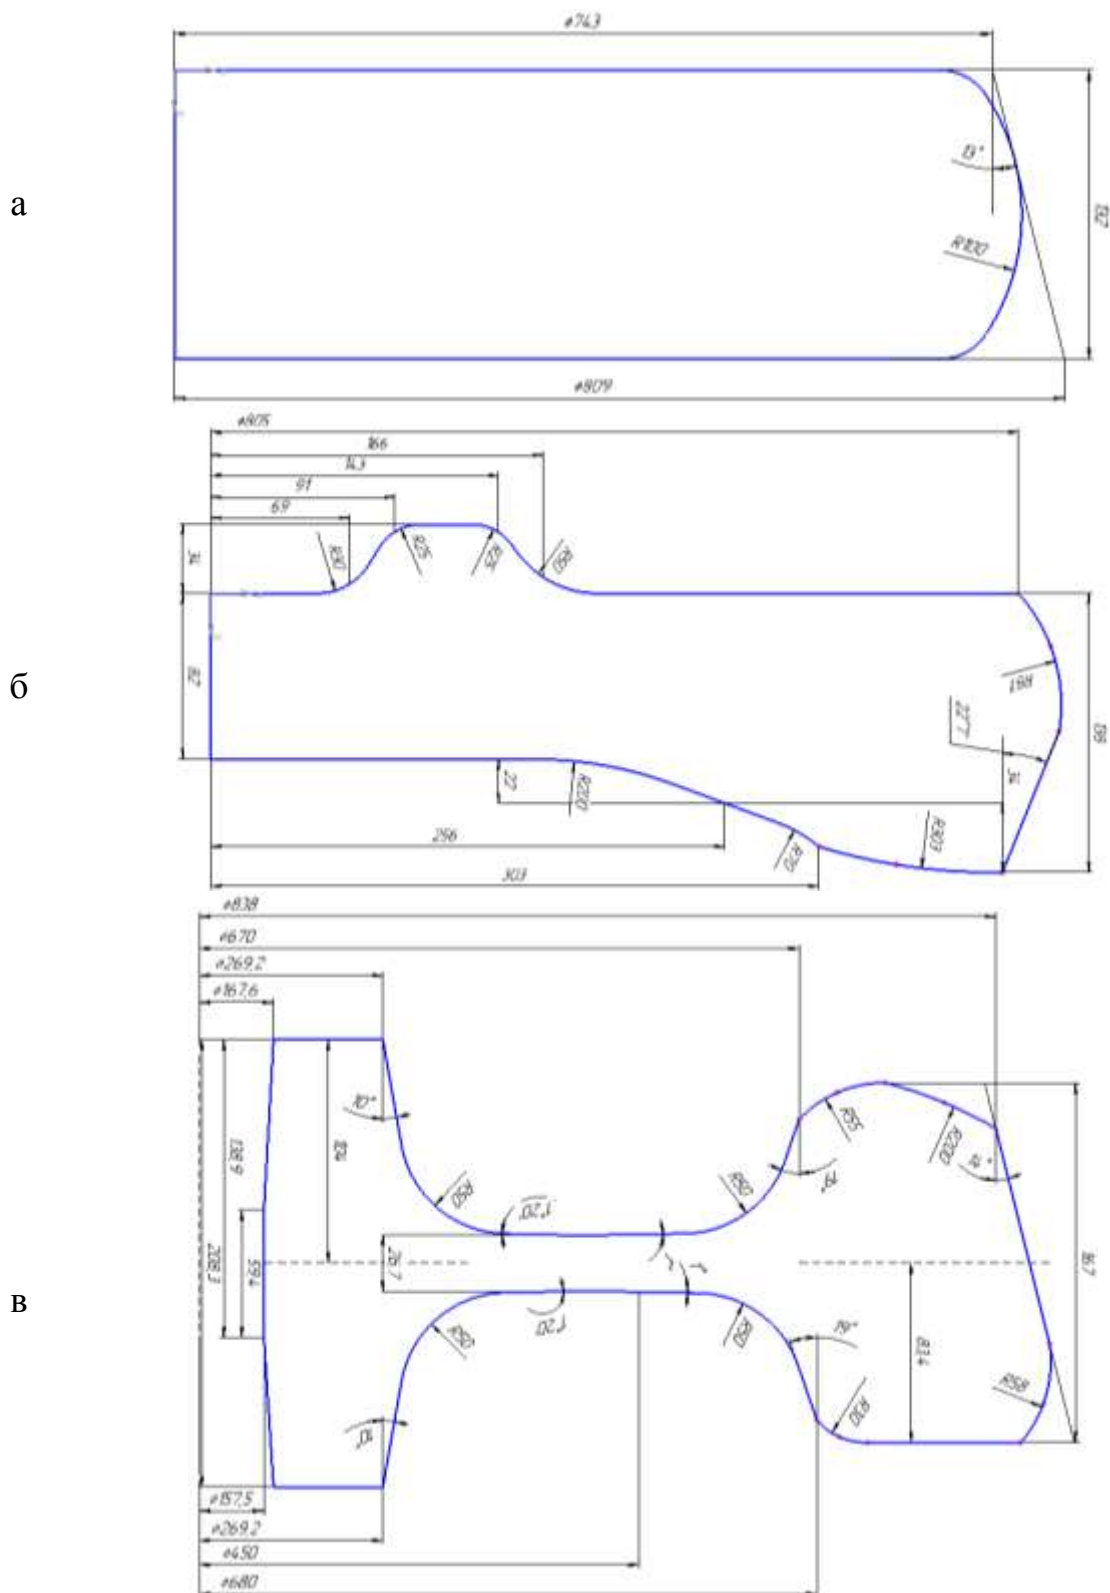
Калибровка по металлу для прессы: а – 20МН; б – 50МН; в - 100МН
